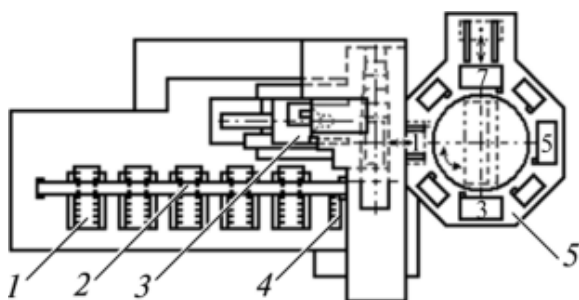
Многоцелевой станок с кассетным инструментальным магазином: 1 — магазинные кассеты; 2 — основная рама; 3 — многоцелевой станок; 4 — инструментальная позиция; 5 — система автоматической смены заготовок
